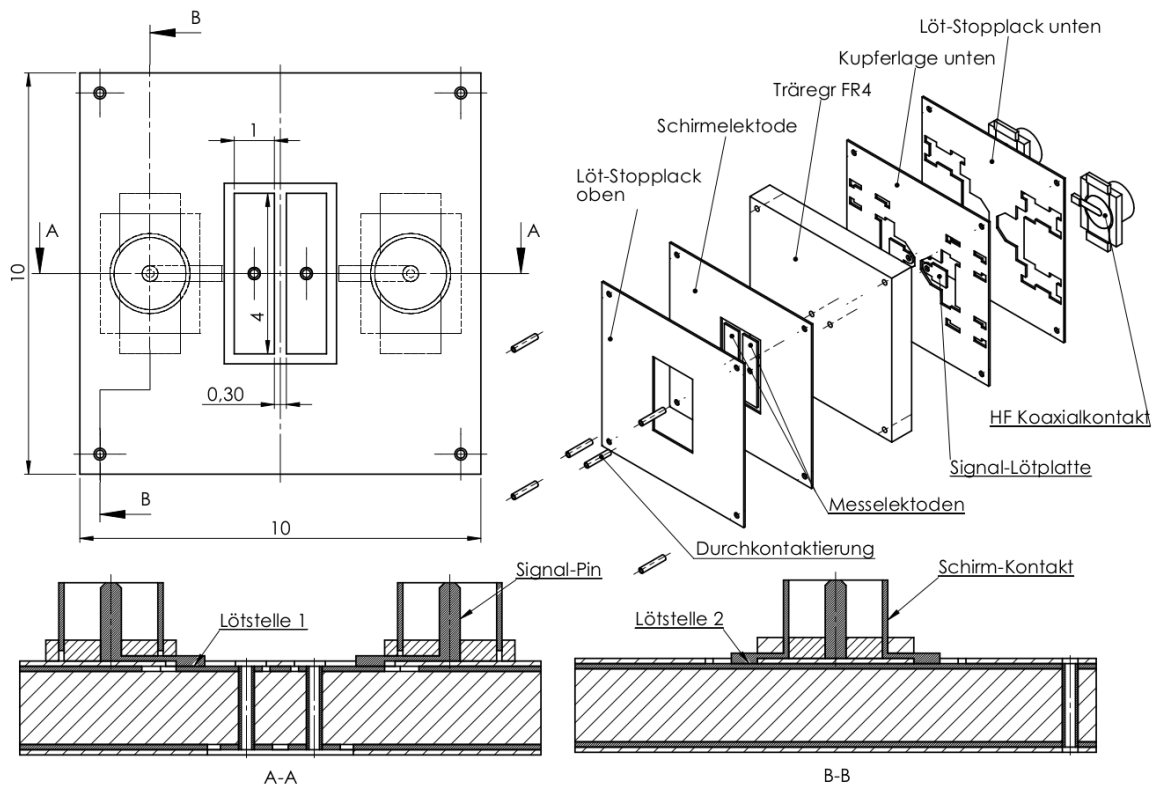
Explosionszeichnung, Aufsicht und Schnittbilder des MPS⁷⁰
